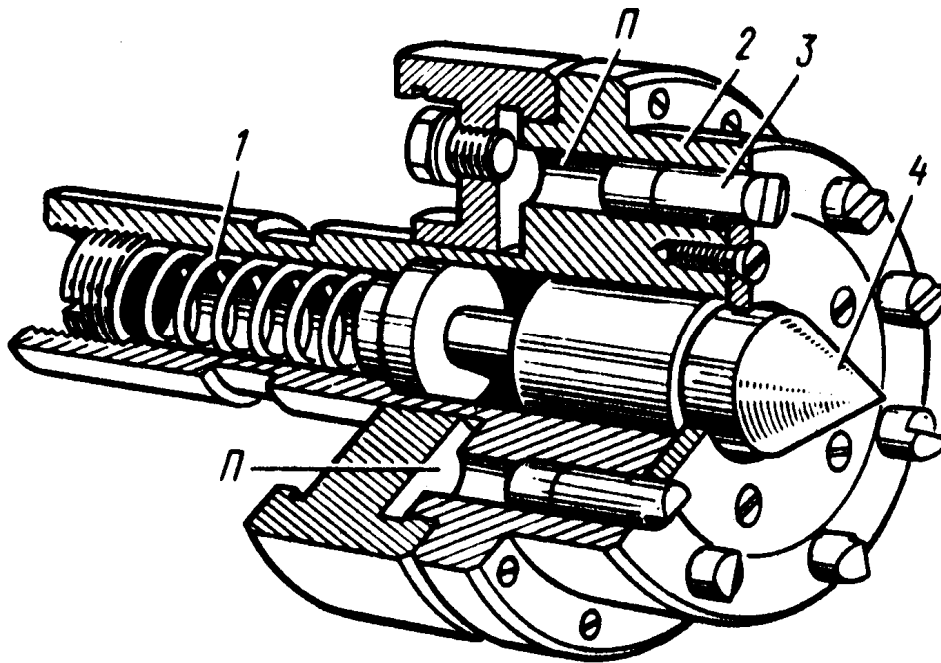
Повідковий патрон з плаваючим центром для верстатів з ЧПК
